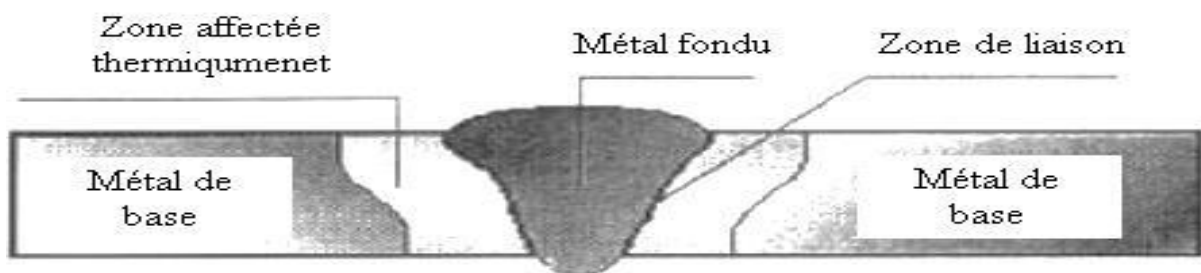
Les différentes zones d'un assemblage soudé.
